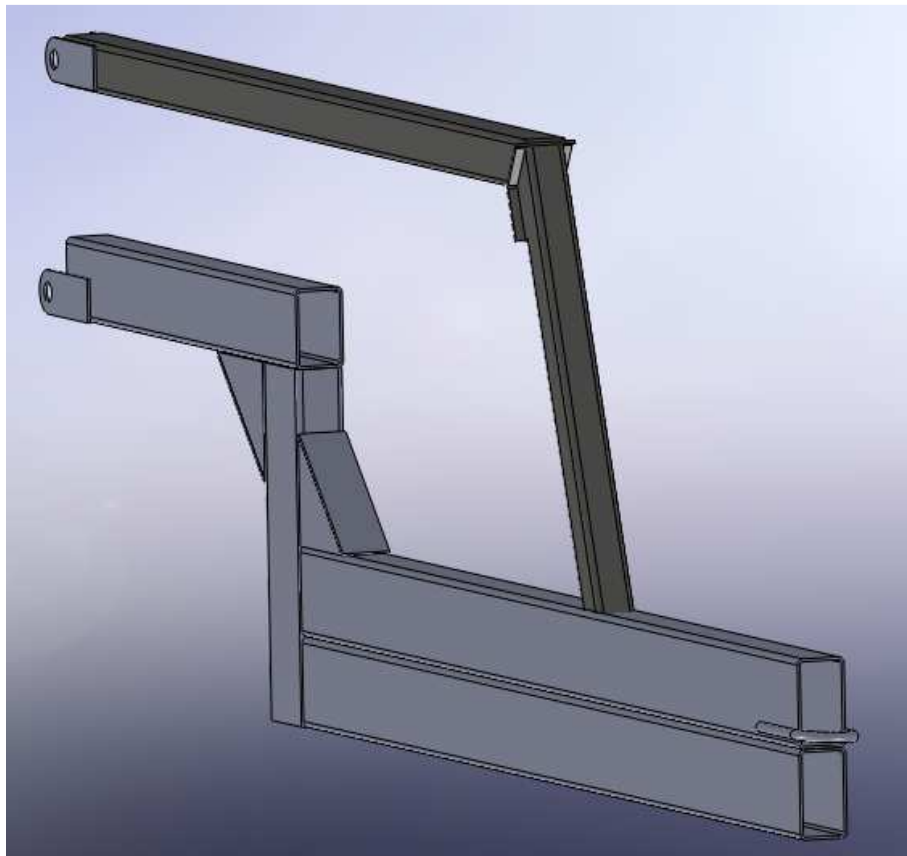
Estrutura de apoio ao ensaio de fecho da ligação pilar-estrado
